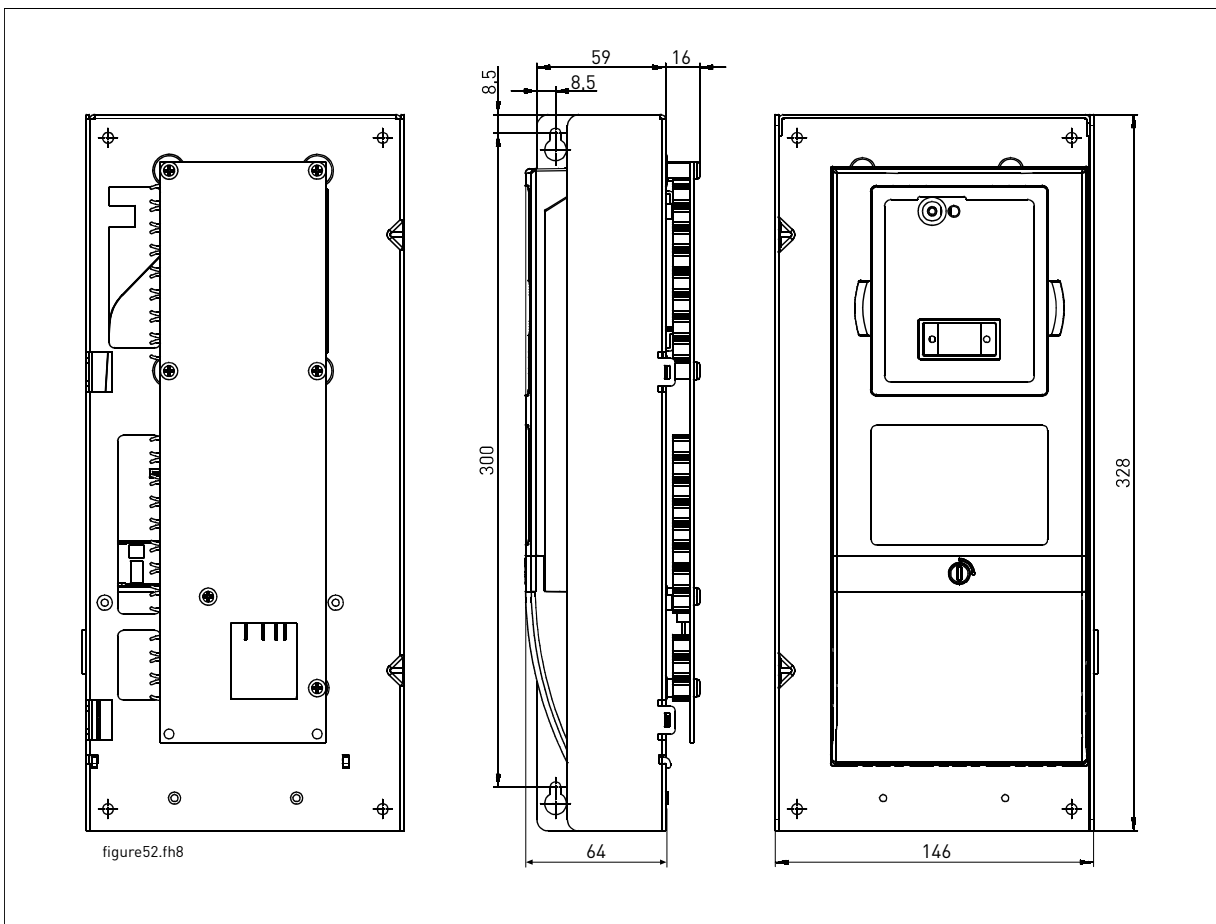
Dimensiones de unidad de control (con tarjeta de acoplamiento estrella conectada, sólo FR12 o FR14)
